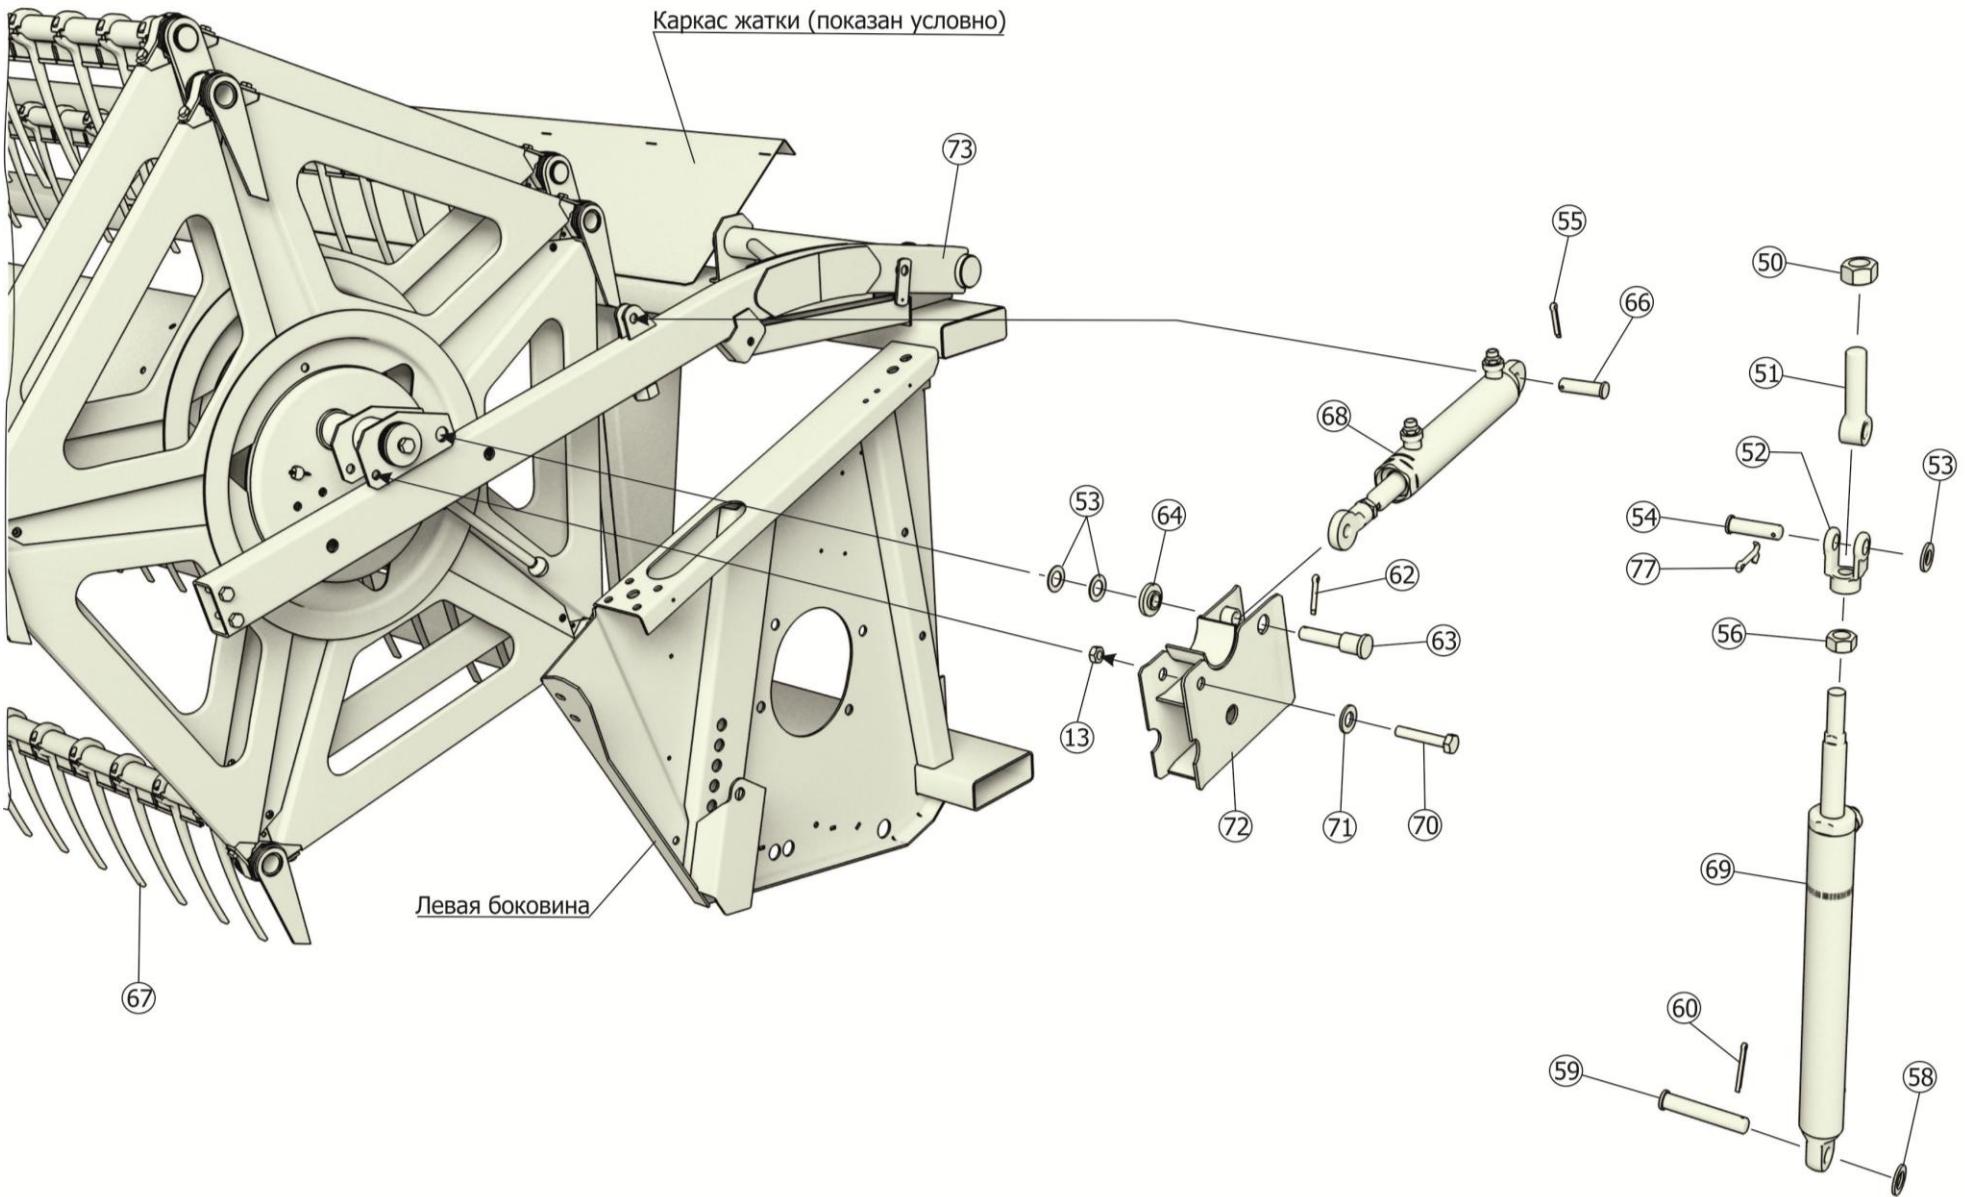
Установка мотовила ЖСУ-900.03.00.000. Вид слева
